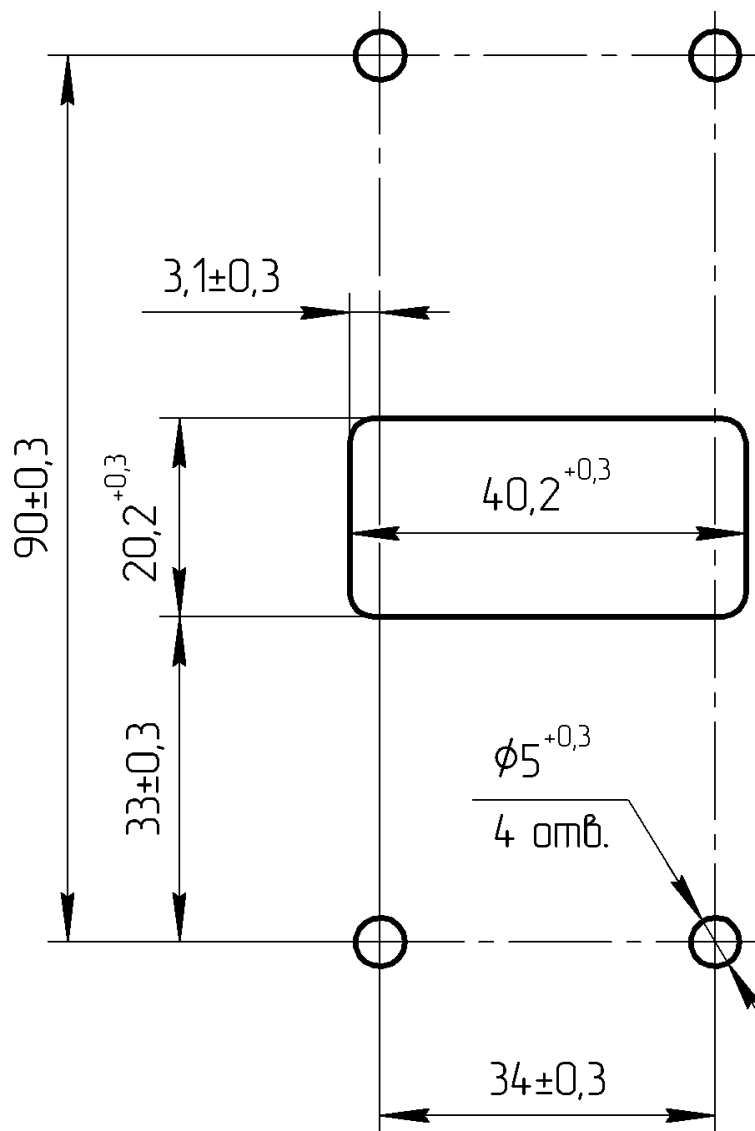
Разметка отверстий для монтажа индикатора выносного тип 1
